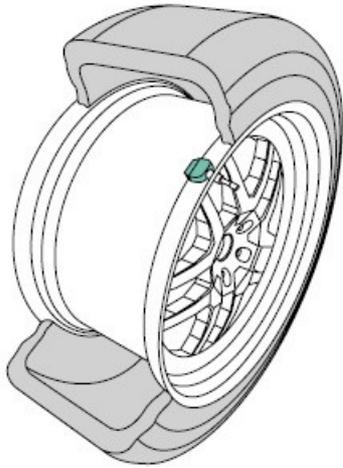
Platzierung des drahtlos betriebenen Pneudruck-Sensors
